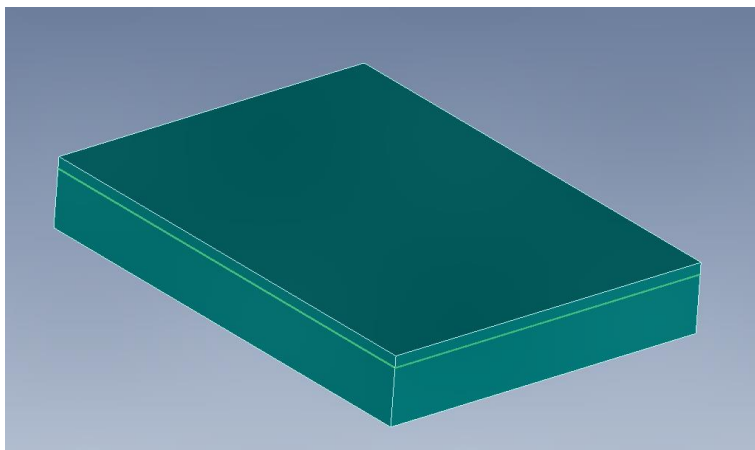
Модель резинометаллического виброизолятора без отверстий
